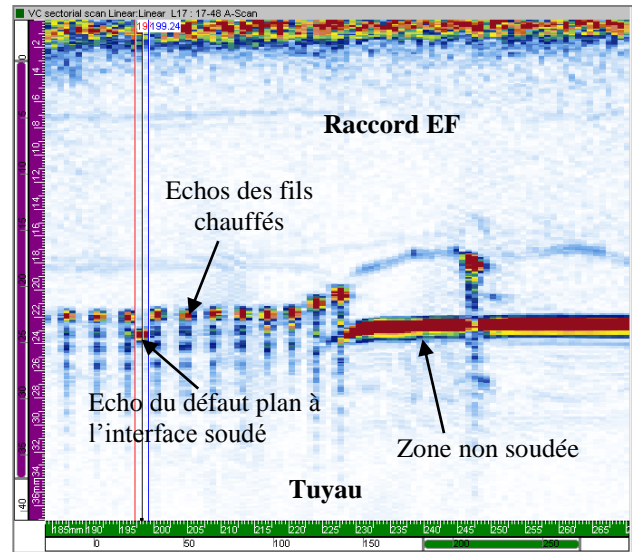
Image ultrasonore d'un joint EF sur tuyau SDR11 de 225 mm de diamètre, contenant un défaut plan de 2 mm à l'interface soudé.
